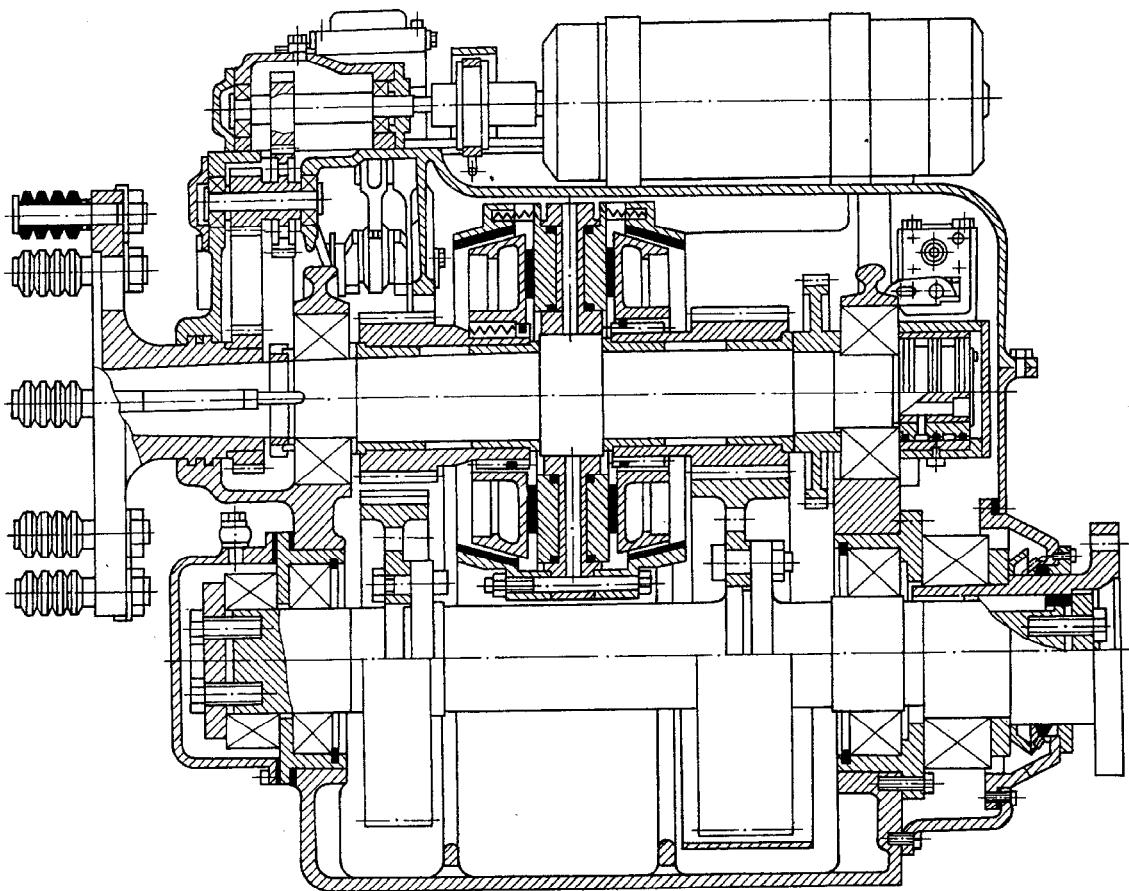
Реверс-редукторная передача 27РРП-230 /продольный разрез/
